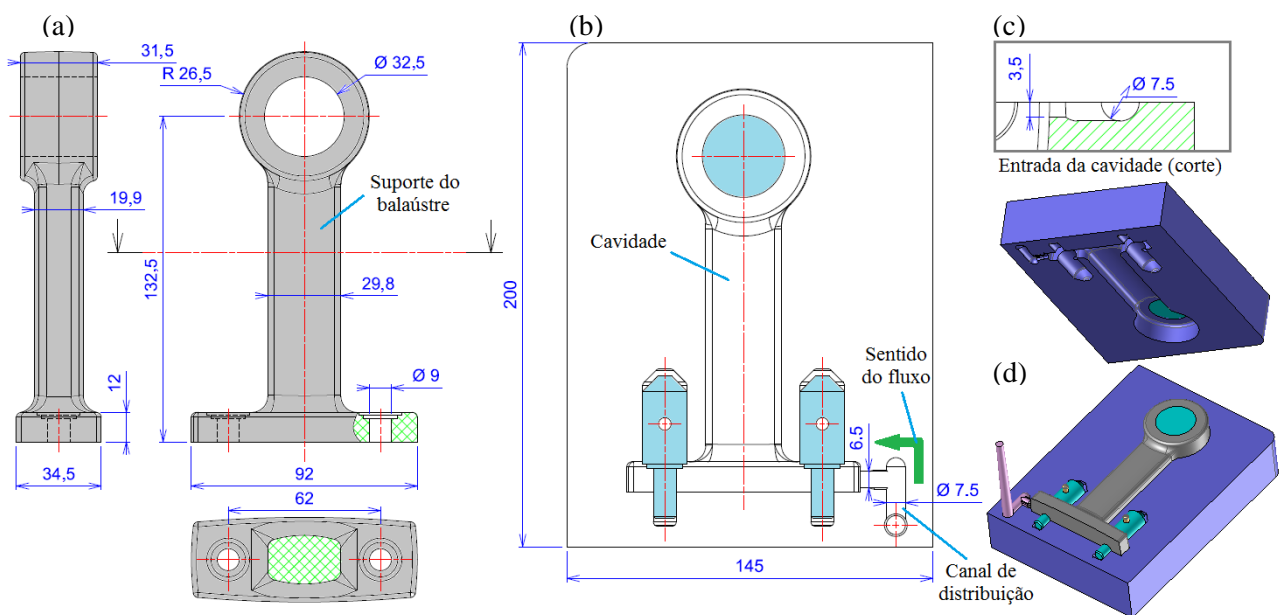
Molde suporte do balaústre. (a) Dimensões do componente. (b) Cavidade e canal de distribuição e entrada. (c) entrada de material em corte, (d) molde e produto em perspectiva.
